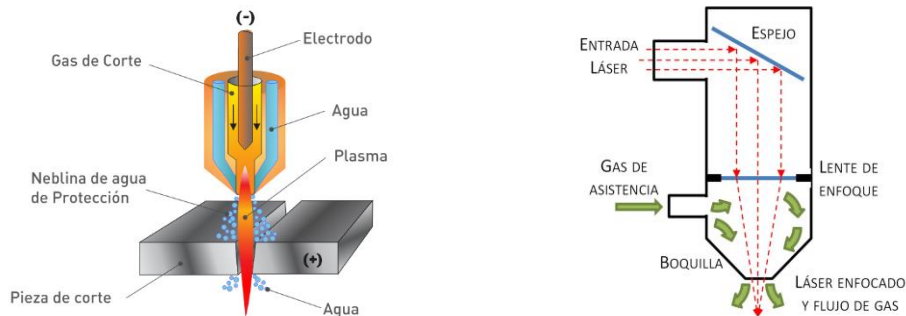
Principios del corte por plasma (izquierda) y láser (derecha)
